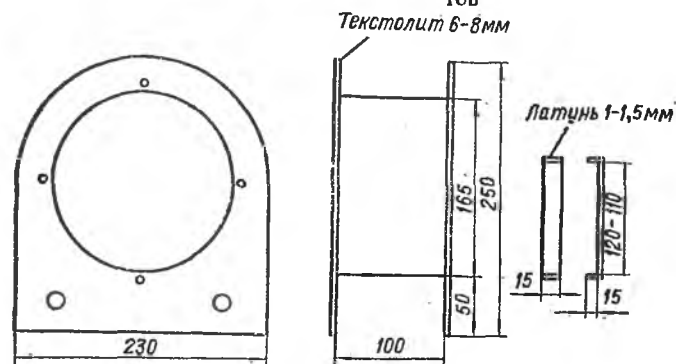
Конструкция катушки частичного размагничивания магнитов
